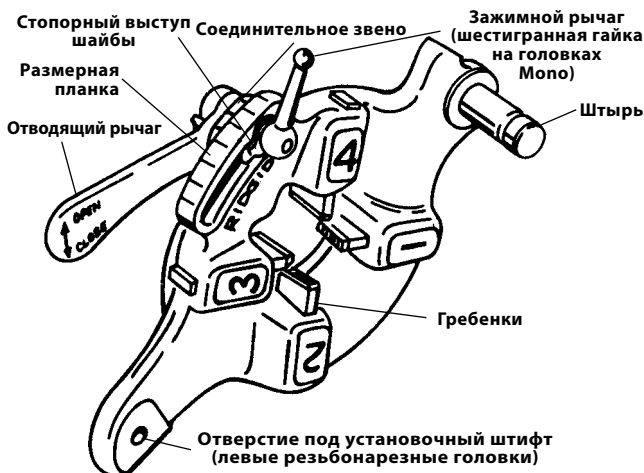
Быстрооткрывающаяся резьбонарезная головка
